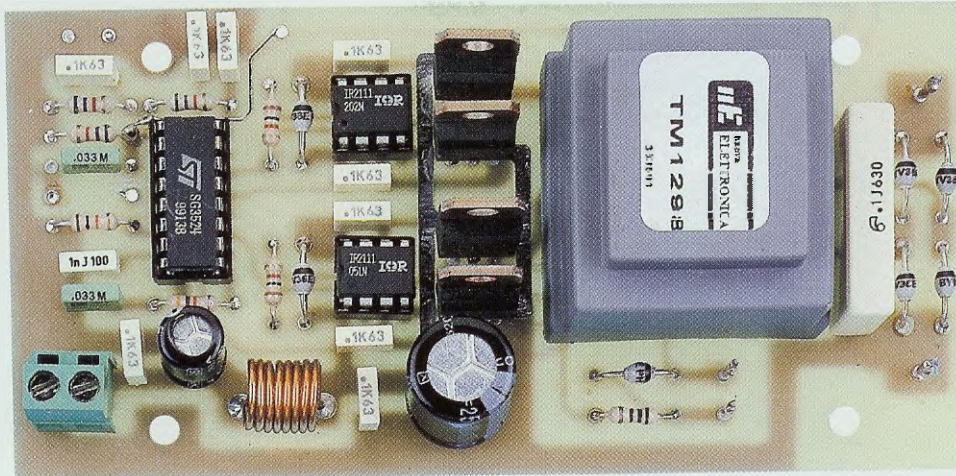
Foto di come si presenta il circuito a montaggio ultimato. Vi ricordiamo che il circuito stampato che vi forniamo assieme al kit è completo di disegno serigrafico e anche di tutte le sigle dei singoli componenti.
